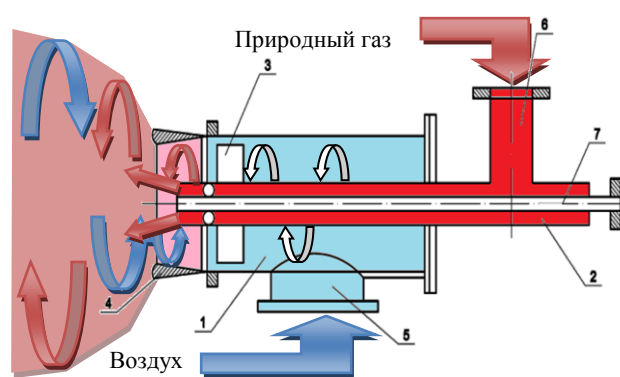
Схема конструкции вихревых газовых горелок: 1 – воздушная камера; 2 – газовая камера; 3 – завихритель; 4 – насадка горелки; 5 – воздушный патрубок; 6 – газовый патрубок; 7 – смотровая труба
